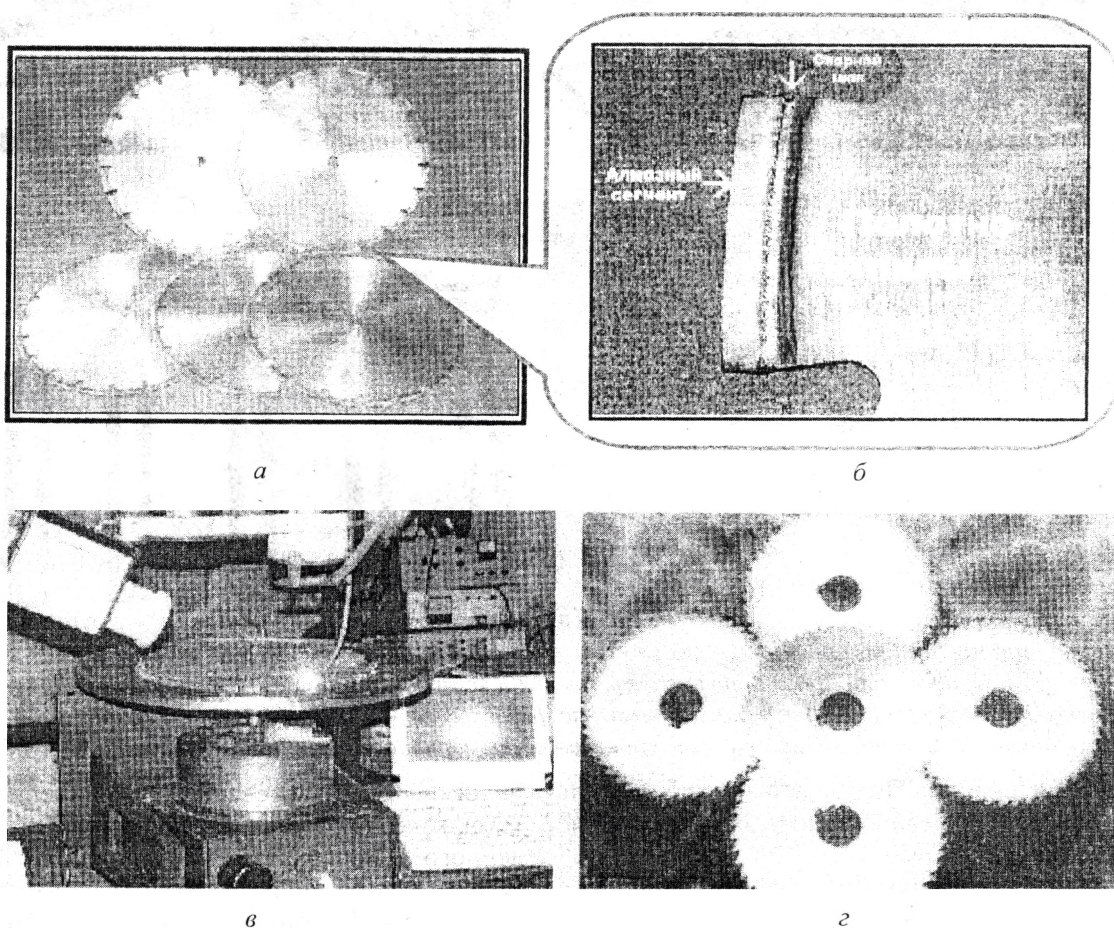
Инструмент, изготовленный с применением лазерной сварки: а-в — лазерная сварка отрезных алмазных сегментных кругов; г — биметаллические фрезы (Р6М5-9ХС), изготовленные с применением лазерной сварки
